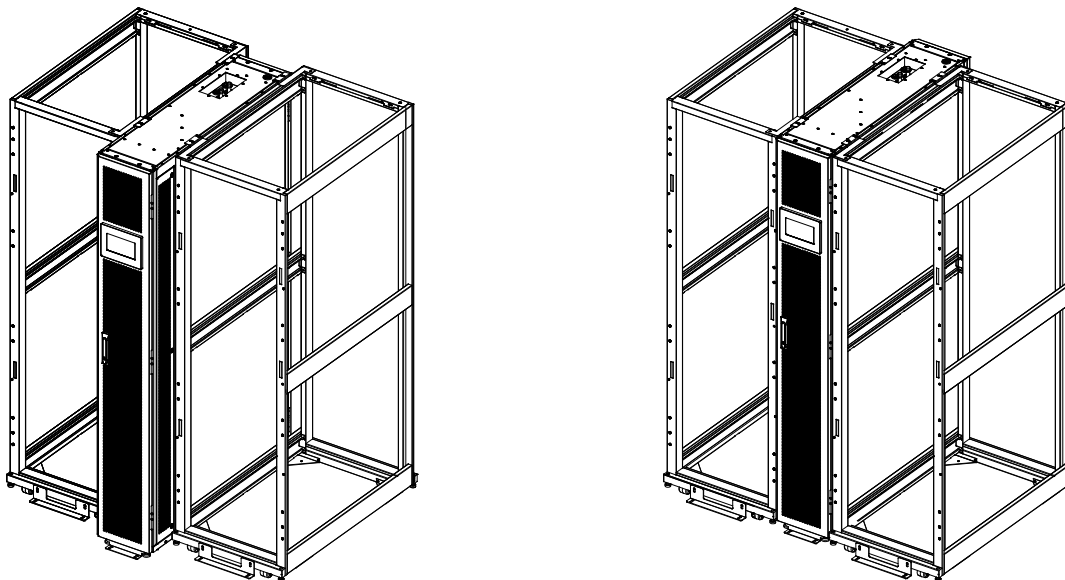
Installation en saillie (à gauche) et encastrée (à droite)
